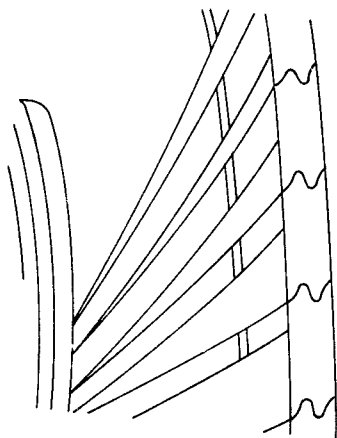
Цельнофрезерованный бандаж с «зубом» для лопаток турбин ЛМЗ
